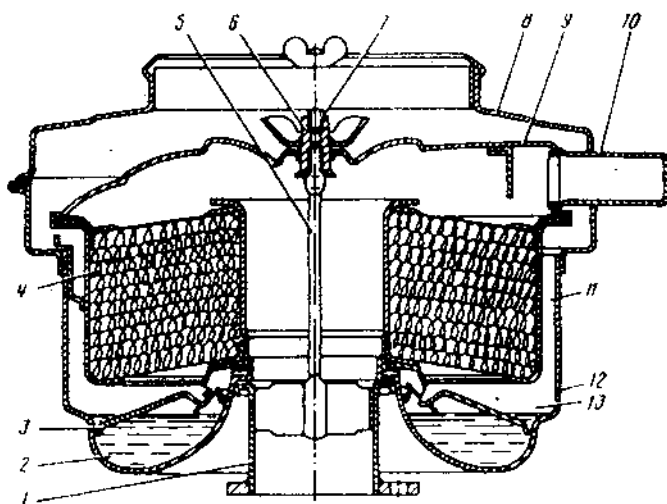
Воздухоочиститель двигателя автомобиля ЗИЛ-130.
